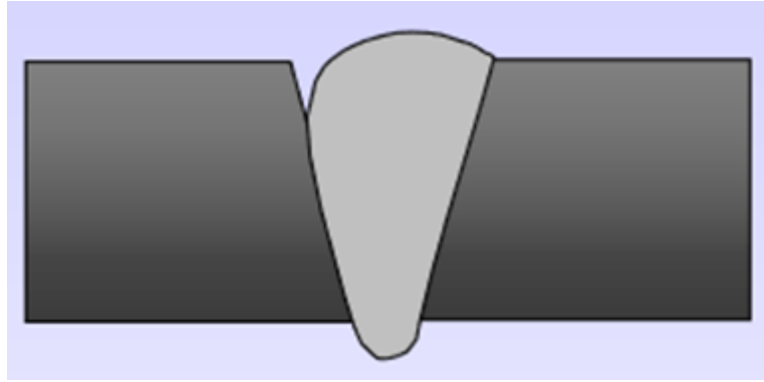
Canelură umplută incompletă. Sursă: M.S. Rogers, Welding Inspection Defects/Repairs Course Reference WIS 5, 2003.
